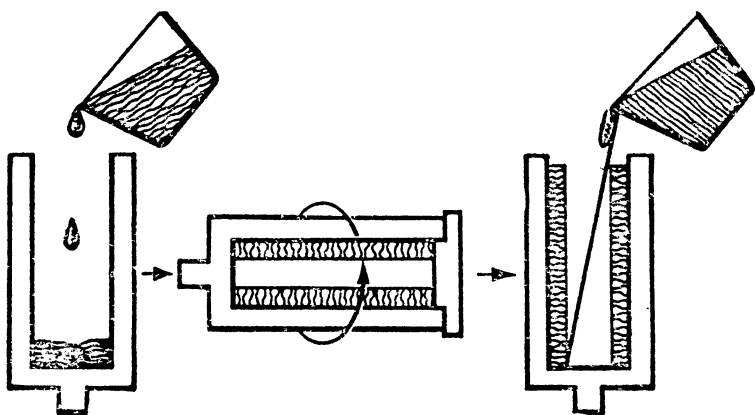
Схема получения двухслойной заготовки сливным методом с вращением
